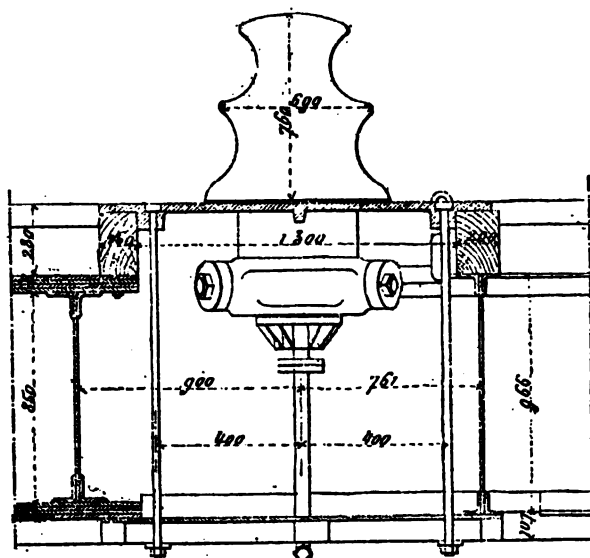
Cabestan hydraulique du Bassin Bellot. — Plan.
